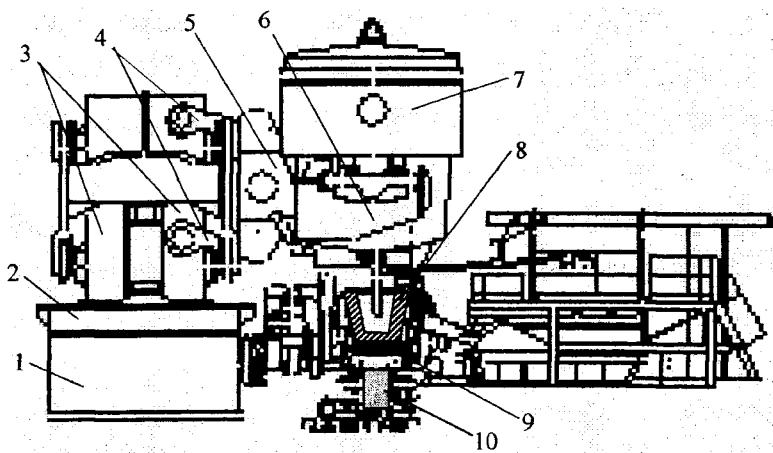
Схема размещения сталеразливочного ковша в рабочей позиции для разливки стали:
